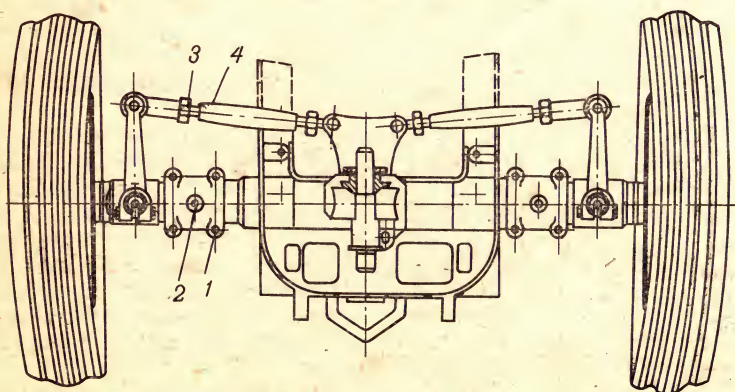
Регулировка колеи передних колес трактора Т-40М:
